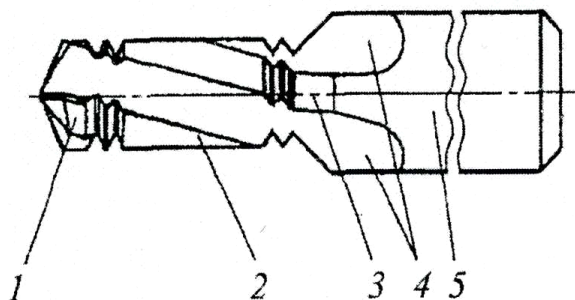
Комбинированный инструмент для получения резьбовых отверстий:
